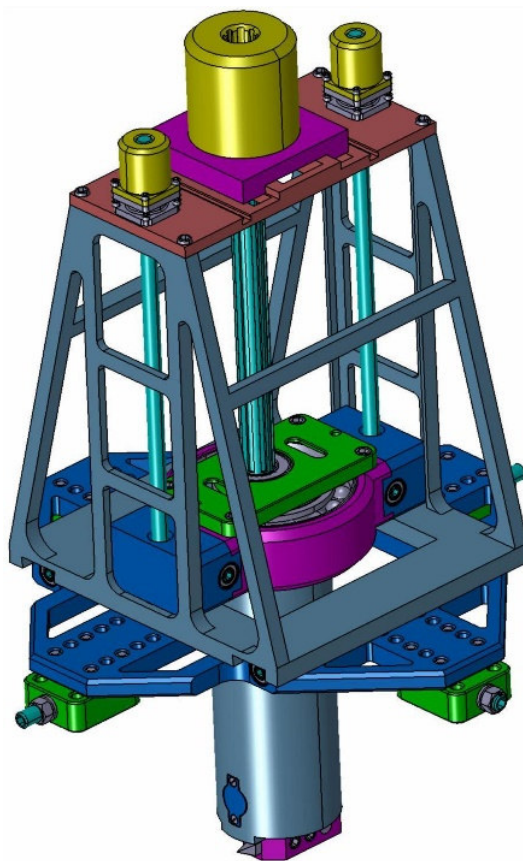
3D-модель мобильного расточного станка для обработки внутренних поверхностей
